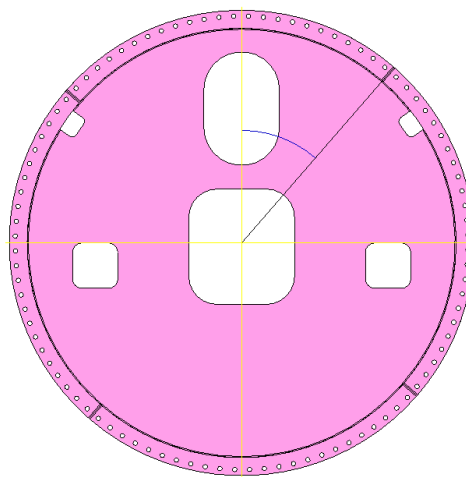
Zobrazení zkosení vnitřního plechu a místo svaru
